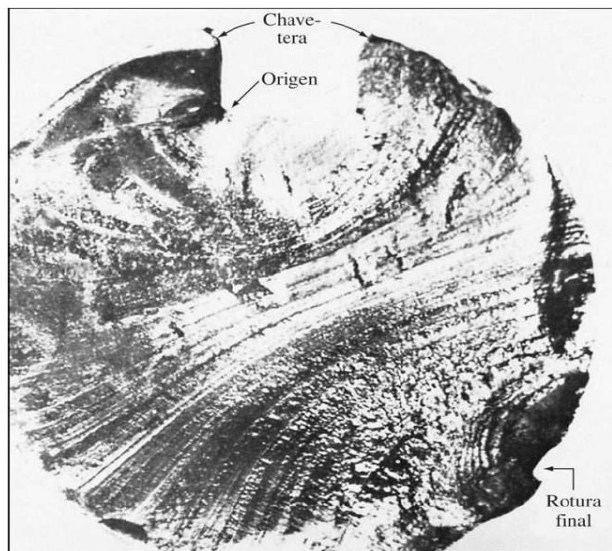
Superficie de fractura por fatiga de un eje fabricado con acero. La fisura por fatiga se originó en la esquina inferior izquierda de la chavetera y se extendió casi completamente por toda la sección transversal antes de que ocurriera la fractura.
